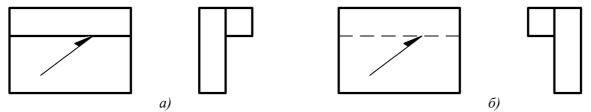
Условные изображения швов сварных соединений: a — видимый шов; δ — невидимый шов
